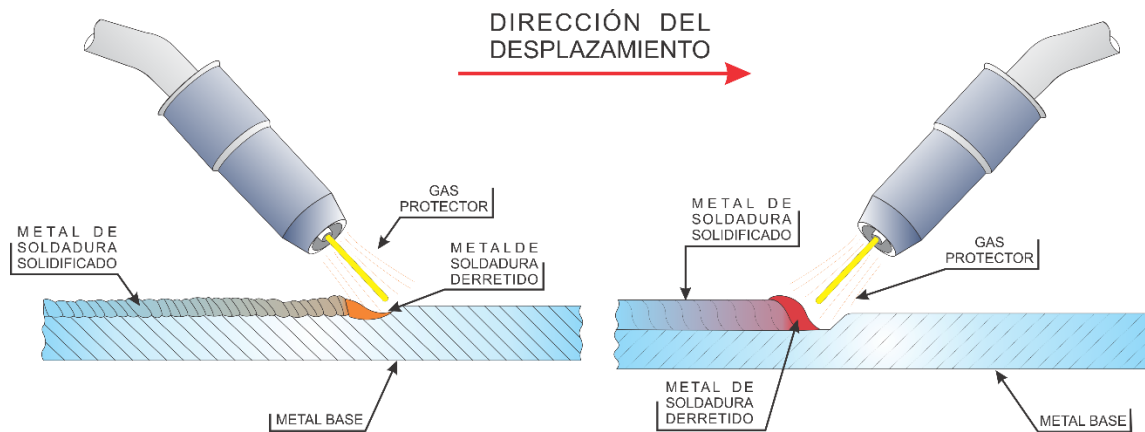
Representación esquemática del ángulo de la pistola utilizado en el proceso de soldadura de arco metálico con protección de gas. En la parte izquierda se encuentra la aplicación de soldadura con un ángulo de empuje y en la derecha con un ángulo de arrastre.
